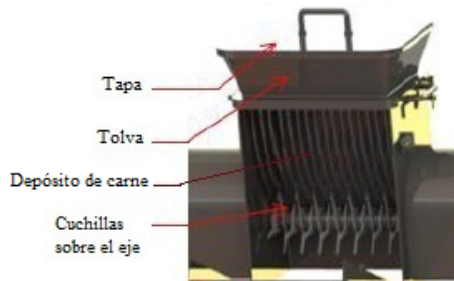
Detalle del conjunto deshebrador hecho en dibujo CAD.
